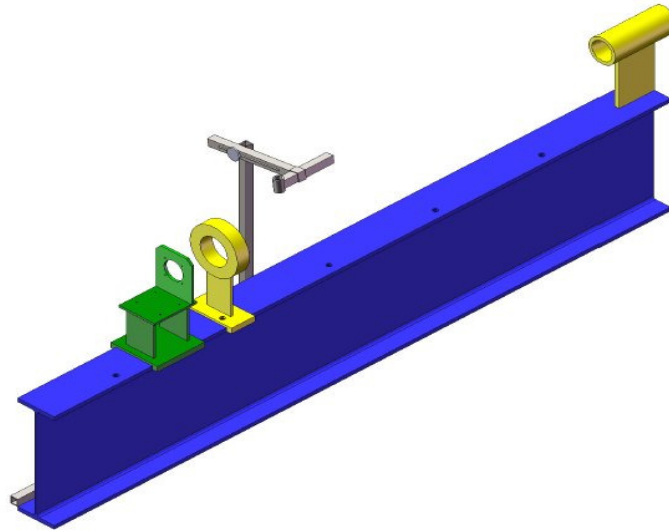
Estrutura do dispositivo automático de soldagem
